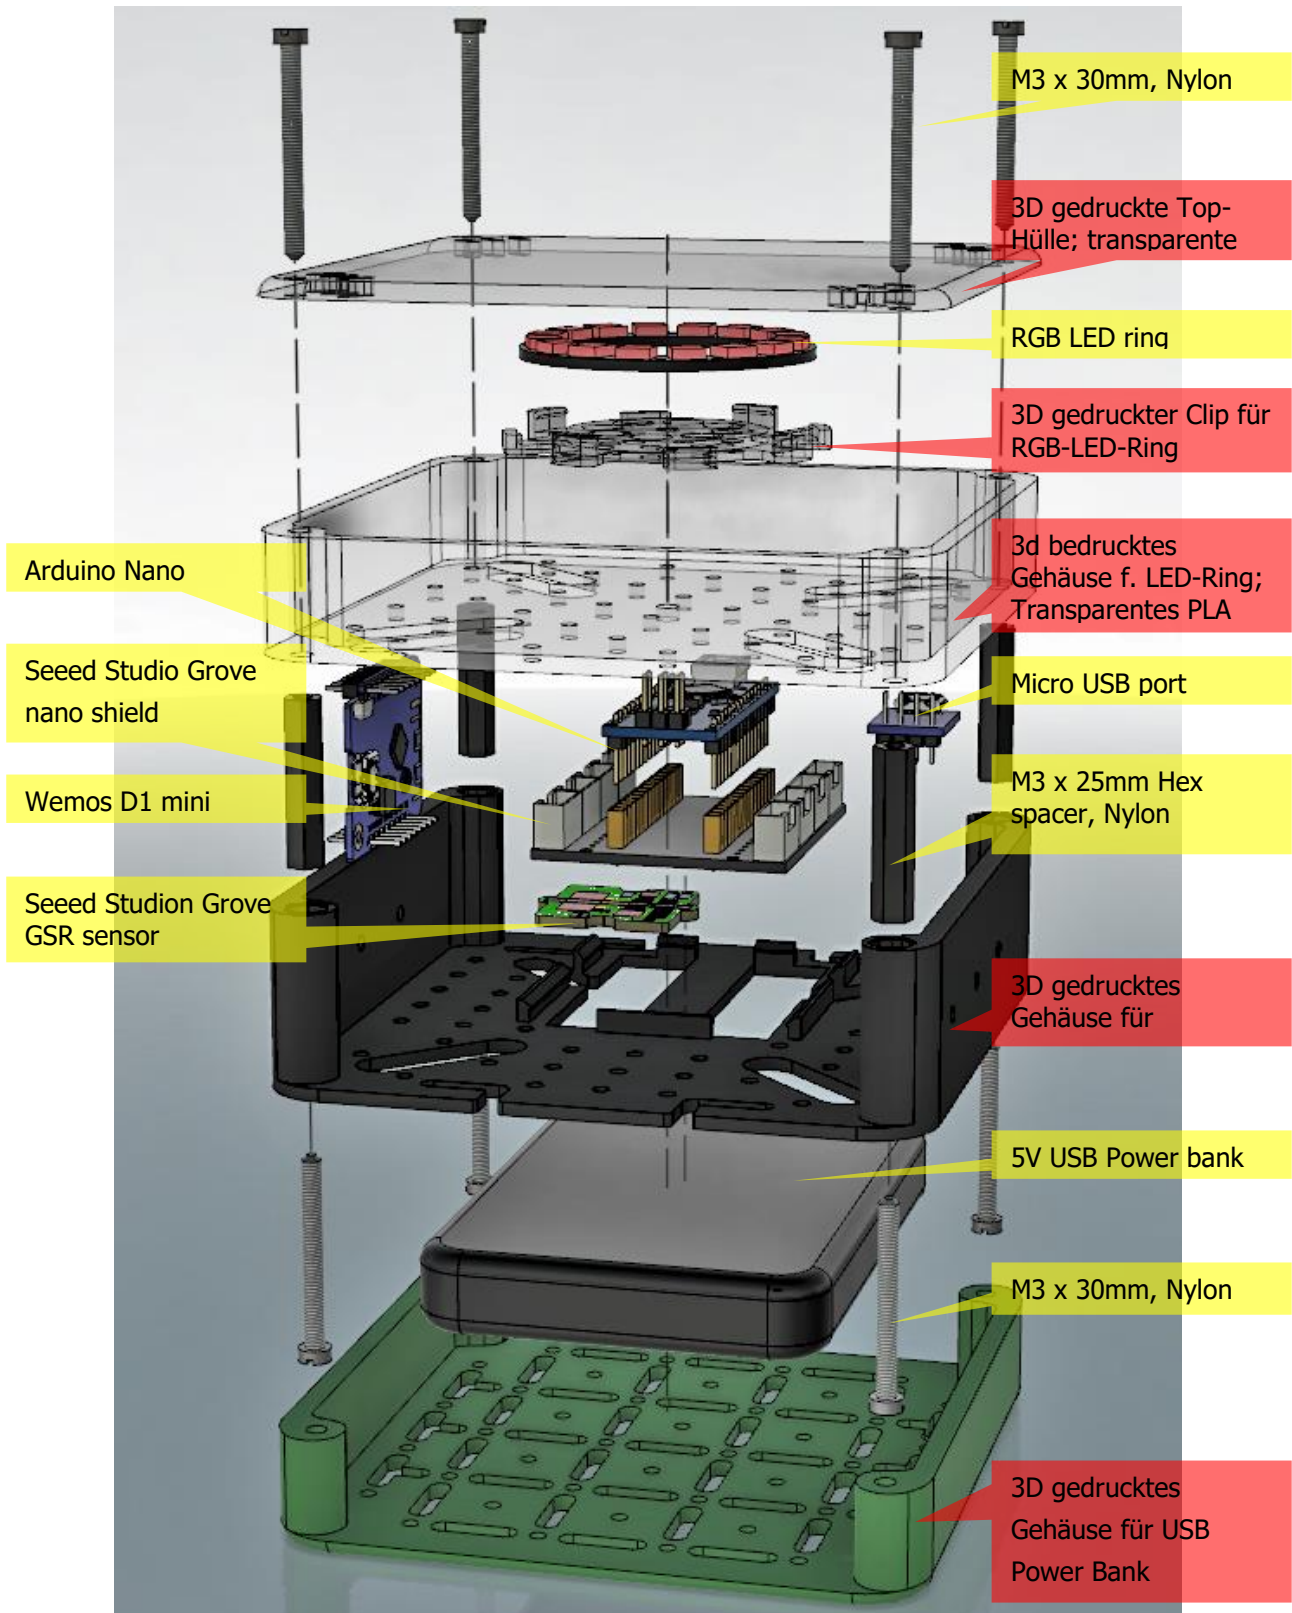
Explosionsbaugruppenzeichnung des Cubes
